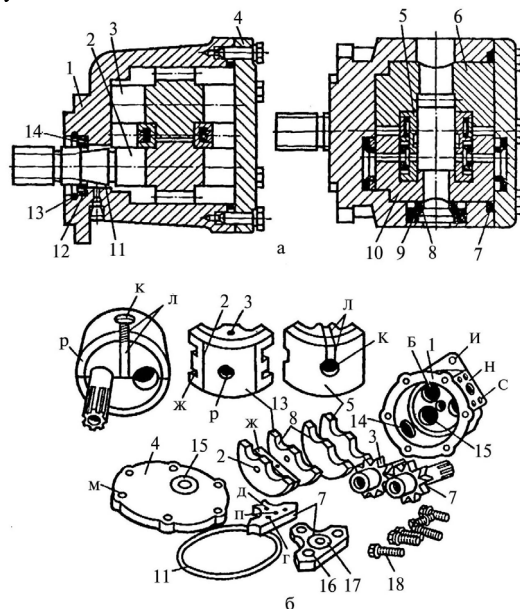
Конструкція насоса типу НШ-К: а - у зібраному вигляді; б - у розібраному вигляді; 1 - корпус; 2 - ведуча шестірня; 3 - ведена шестірня; 4 - кришка насоса; 5 - пластики-замикателі; 6-підшипникова обойма; 7 - ущільнювальне кільце кришки насоса; 8-опорна пластина; 9-манжета радіального піджима; 10 - підтискна обойма; 11- центруюча втулка; 12 - ущільнювальні манжети ведучого вала; 13 - опорне кільце ущільнювальної манжети; 14- пружинне кільце; 15-манжета діаметром 39 мм; 16 - манжета; 17 - манжета діаметром 29 мм; 18 - гвинти з пружинними шайбами; в - виточення під цапфи шестерень; г - отвір діаметром 6 мм; д-росточка діаметром 6 мм і глибиною 2 мм; е - косі отвори; ж - пази під пластики-замикателі; з - трикутні пази; і - отвори для кріплень насоса; к – усмоктувальний отвір; л - канавка для відводу витоків; м- отвори під болти 18; н-площини для кріплення приєднувальної арматури; о - широка фаска; п-отвір діаметром 6 мм; р - нагнітальний отвір; с - отвір для кріплення косинця (арматура).
